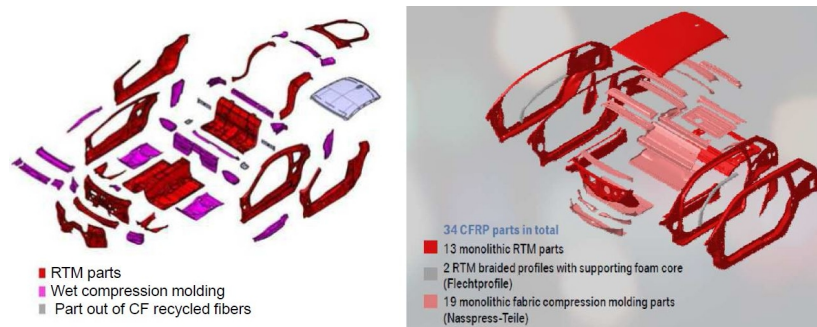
Despieces de chasis de BMW i8 (izquierda) y BMW i3 (derecha) [124].
